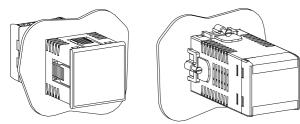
Монтаж прибора щитового крепления Щ5
